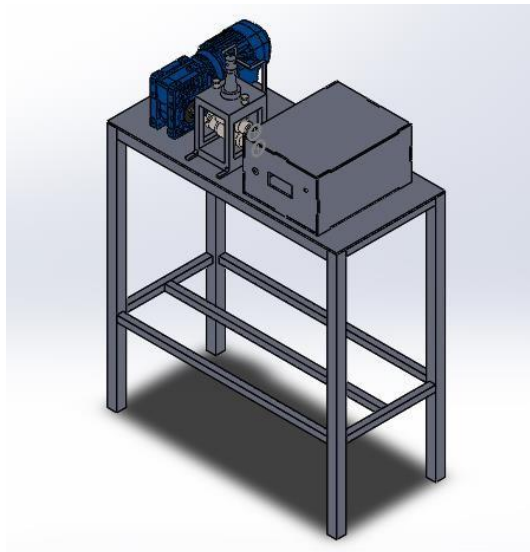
Diseño de la laminadora y motor en posición horizontal.
